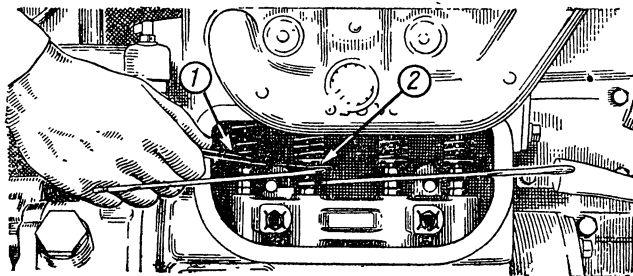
Регулировка зазоров клапанов пускового двигателя:
